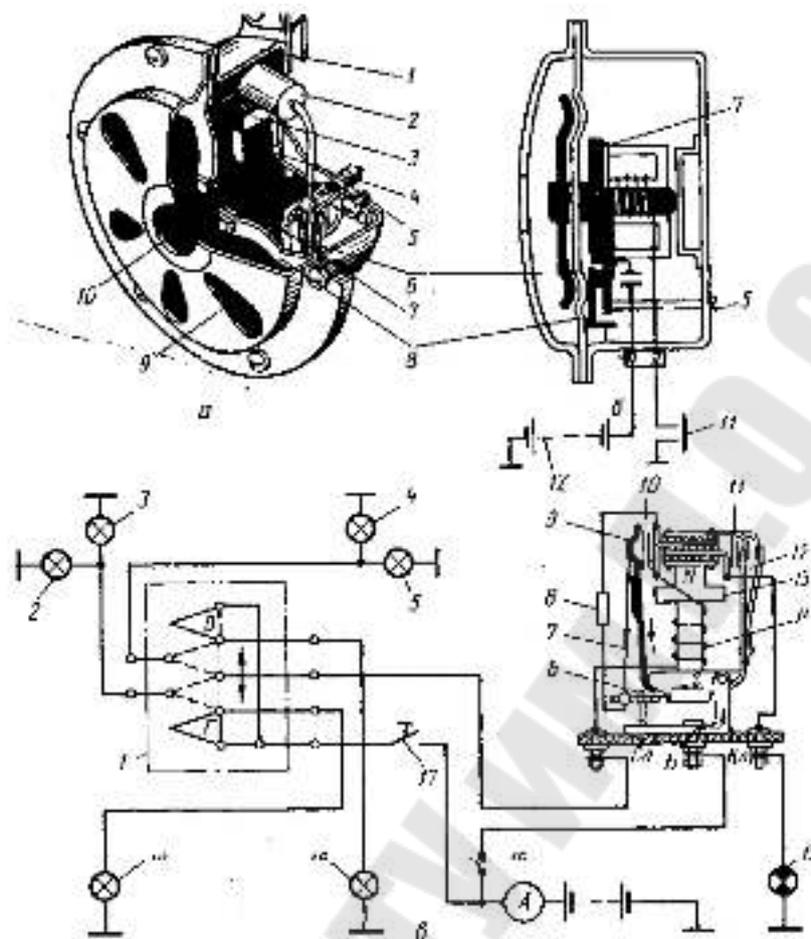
Звуковой сигнал и прерыватель указателей поворота
